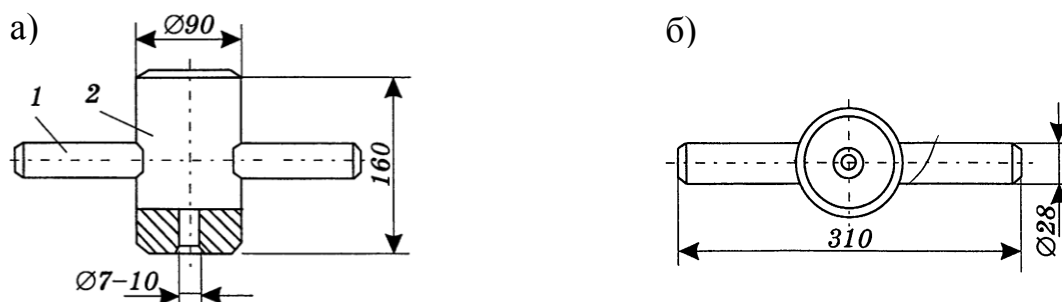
Устройство для забивки и извлечения электродов: а – вид сбоку; б – вид сверху; 1 – рукоятка; 2 – молот.
